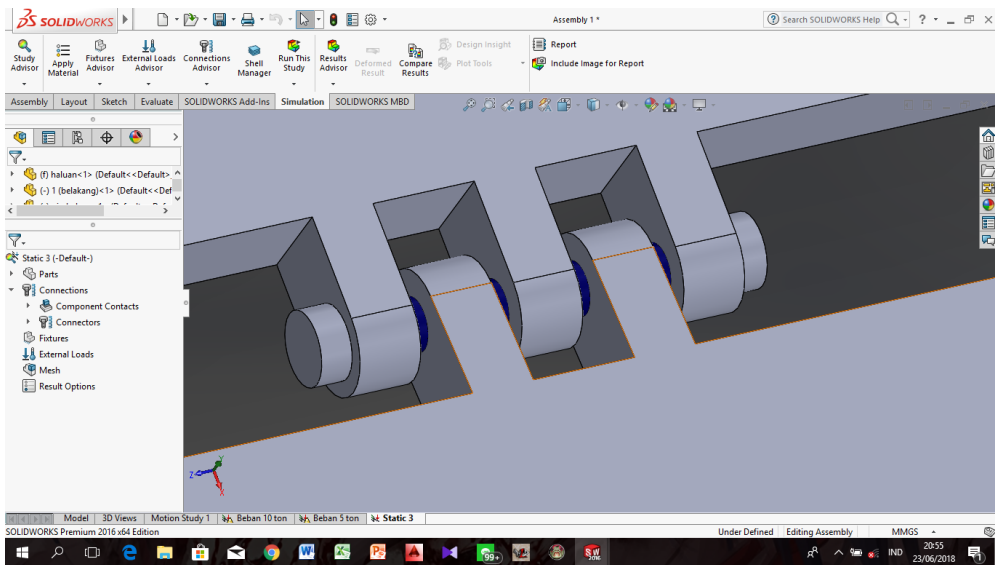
Model Solidworks ramp door pada bagian depan.
